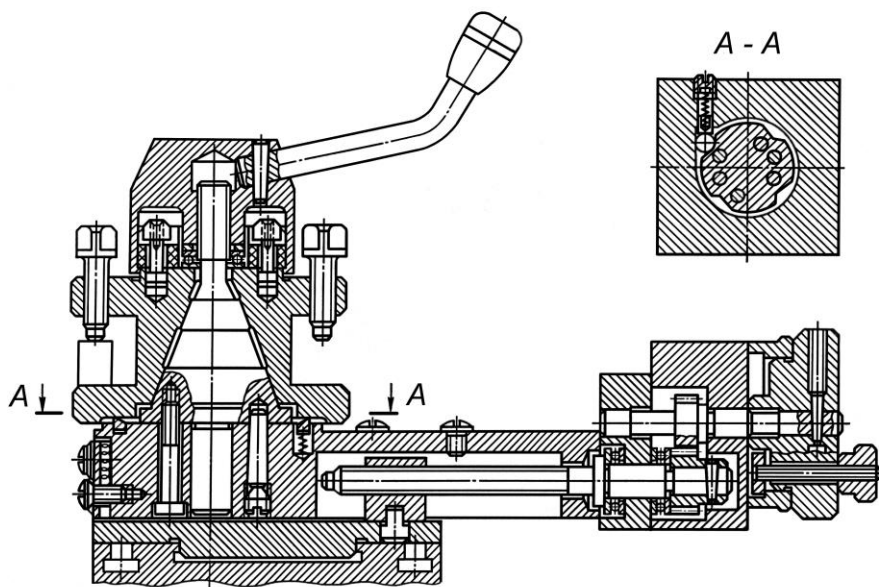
Верхний суппорт с 4-позиционным резцедержателем
